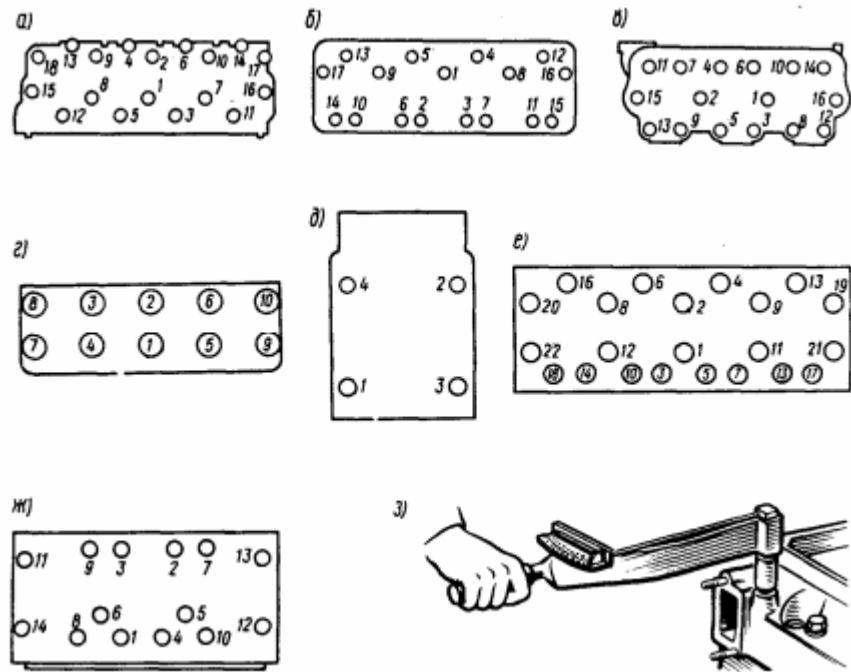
Порядок затяжки болтов (гаек) крепления головки блока цилиндров двигателей автомобилей: а – ГАЗ-53-12; 66-11; -14 «Чайка»; б – ЗИЛ-130, Урал-375Д, автобусы ЛиАЗ-677, ЛАЗ-695Н, – 699Р; в – МАЗ-5335; г – ГАЗ-24, -3102 «Волга»; д – КамАЗ-5320; е – ЗИЛ-4331; ж – Икарус-260; з – торцовый ключ с динамометрической рукояткой
